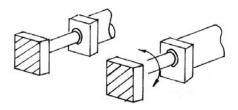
Позиционирование корпуса стиральной машины на станции сварки
